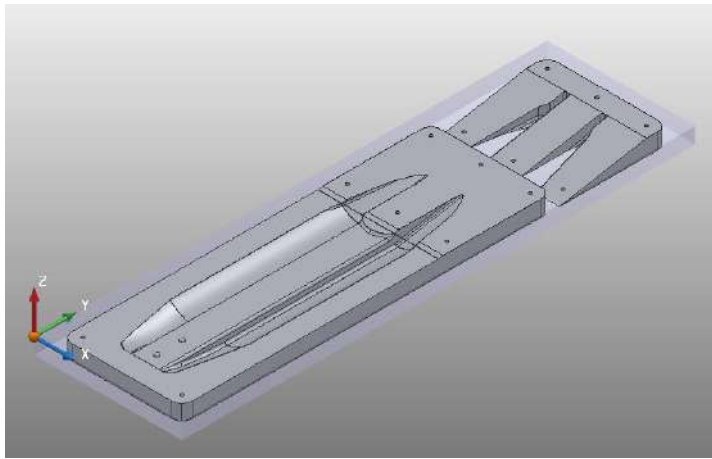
Заготовка под оснастку Габариты: В x Ш x Д=30x280x970 мм
